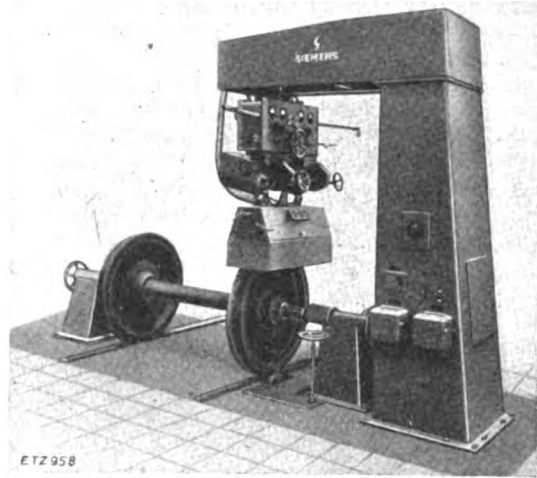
Selbsttätige Spurnschweißeinrichtung mit zwei Schweißköpfen.
